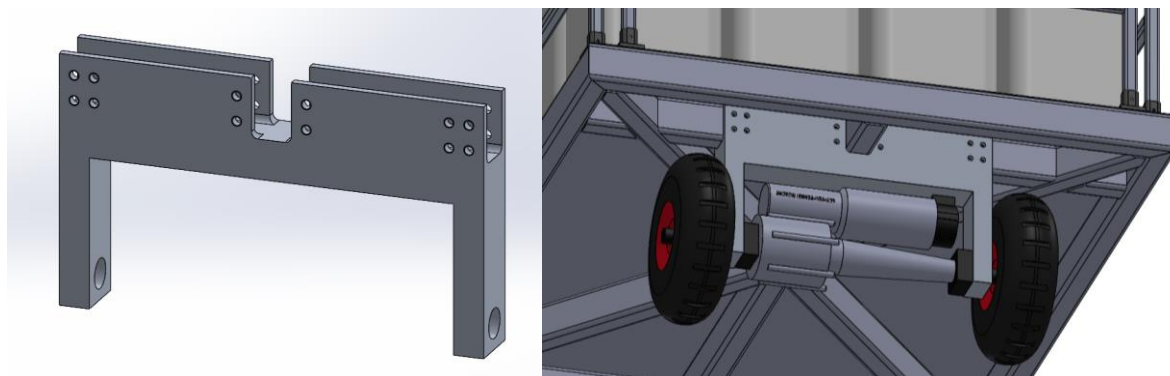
Modelo CAD de la pieza de unión MOTOR-CHASIS y su disposición en el carro [fuente propia]
